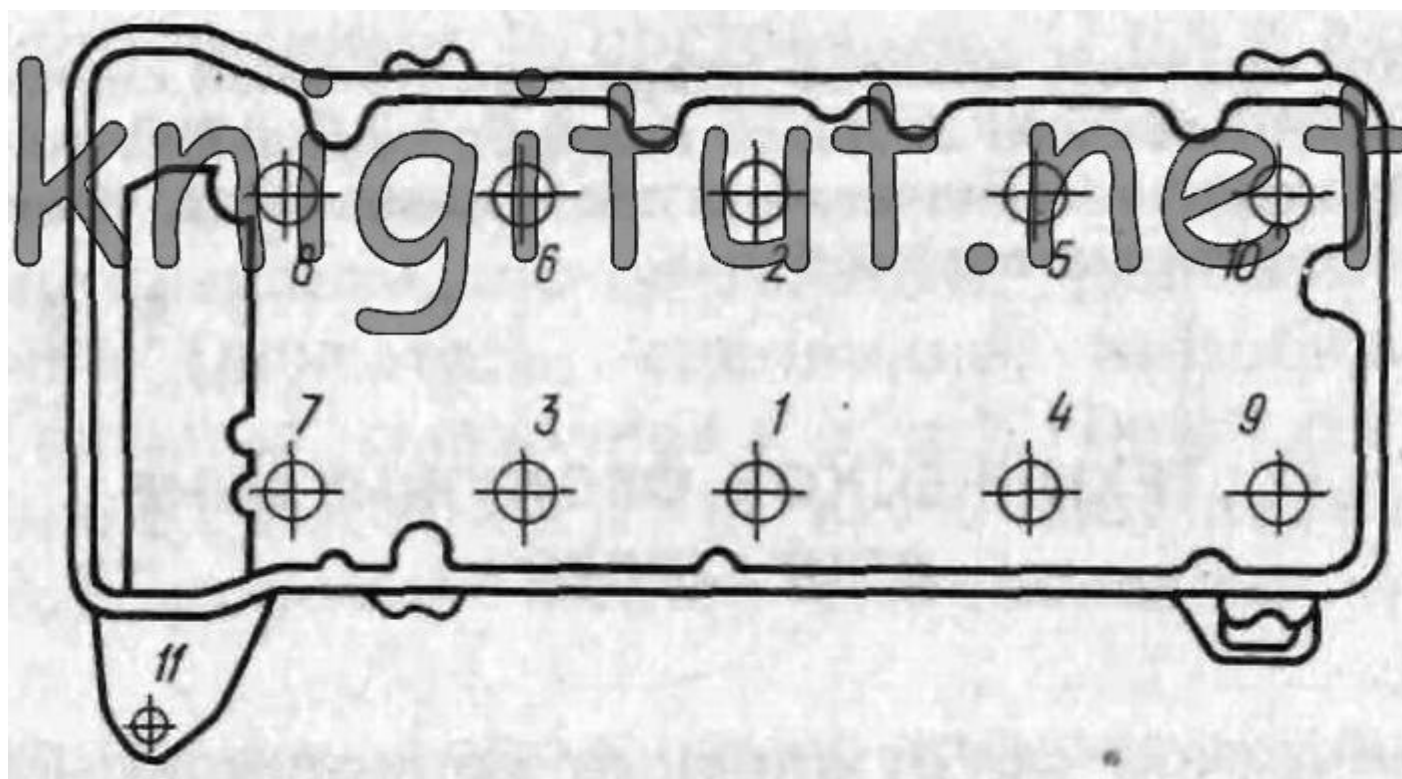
Порядок затягивания болтов крепления головки блока цилиндров
